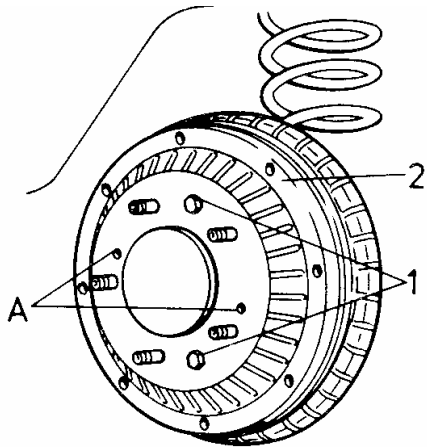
Freno trasero: A- agujeros; 1- tornillos; 2- tambor de freno
